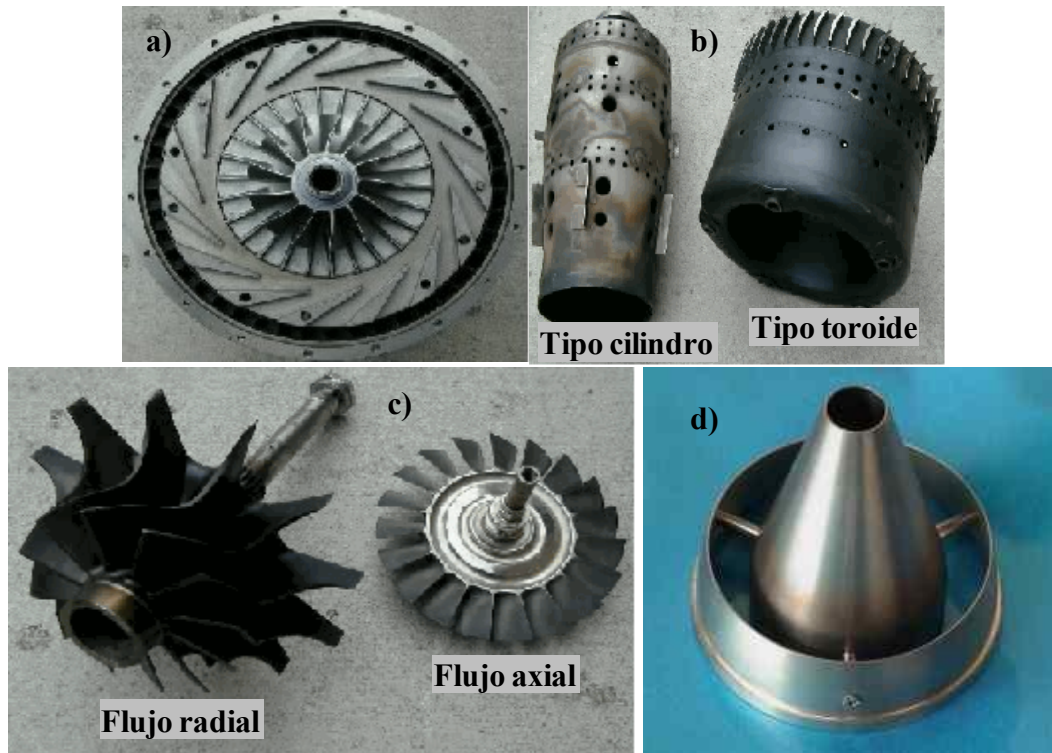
2 - Principales partes que constituyen una turbina de combustión de gas: a) compresor, b) cámaras de combustión, c) turbinas y d) tobera de escape.
